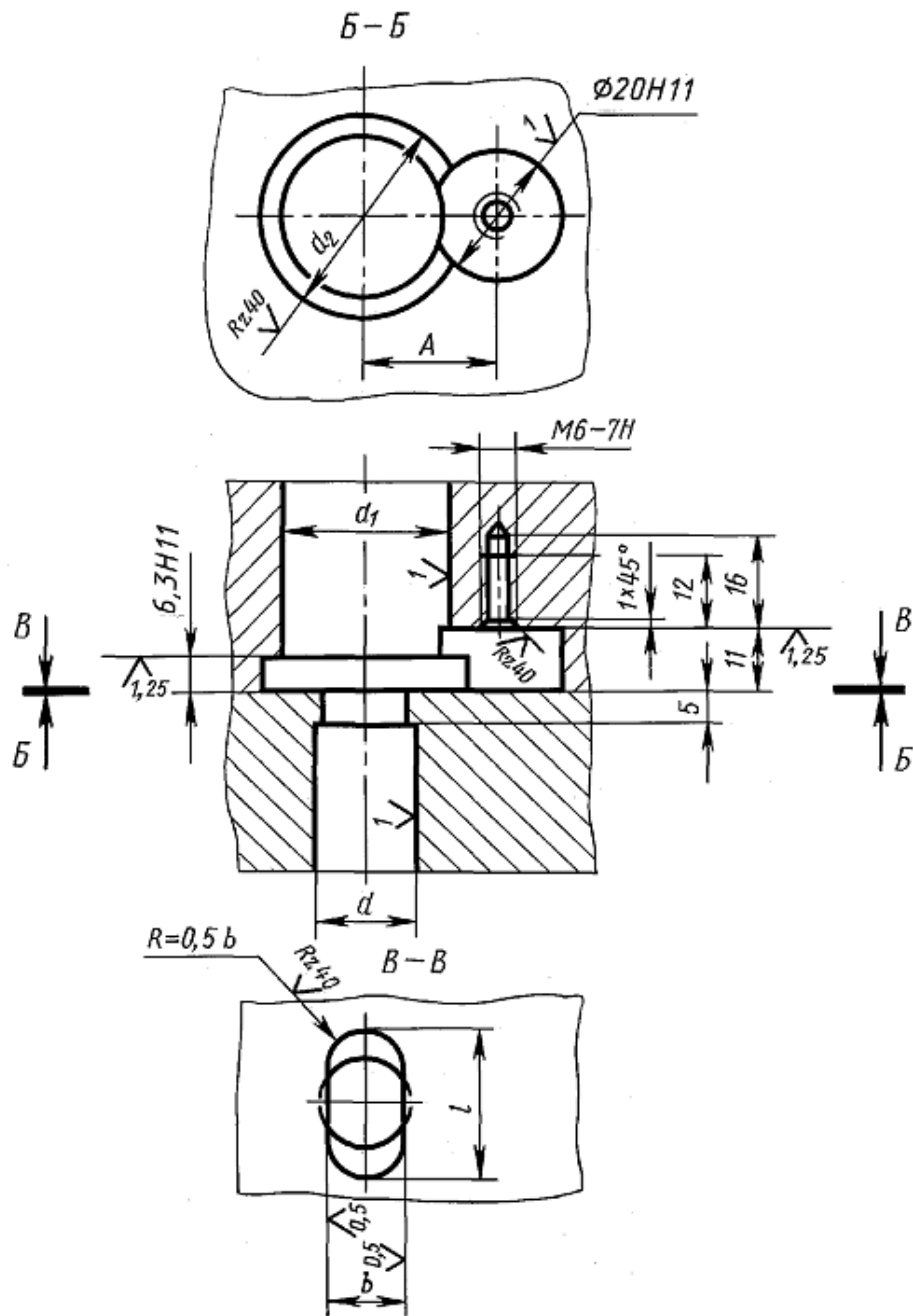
Конструкция гнезд для установки центрирующих соединений с зажимом
